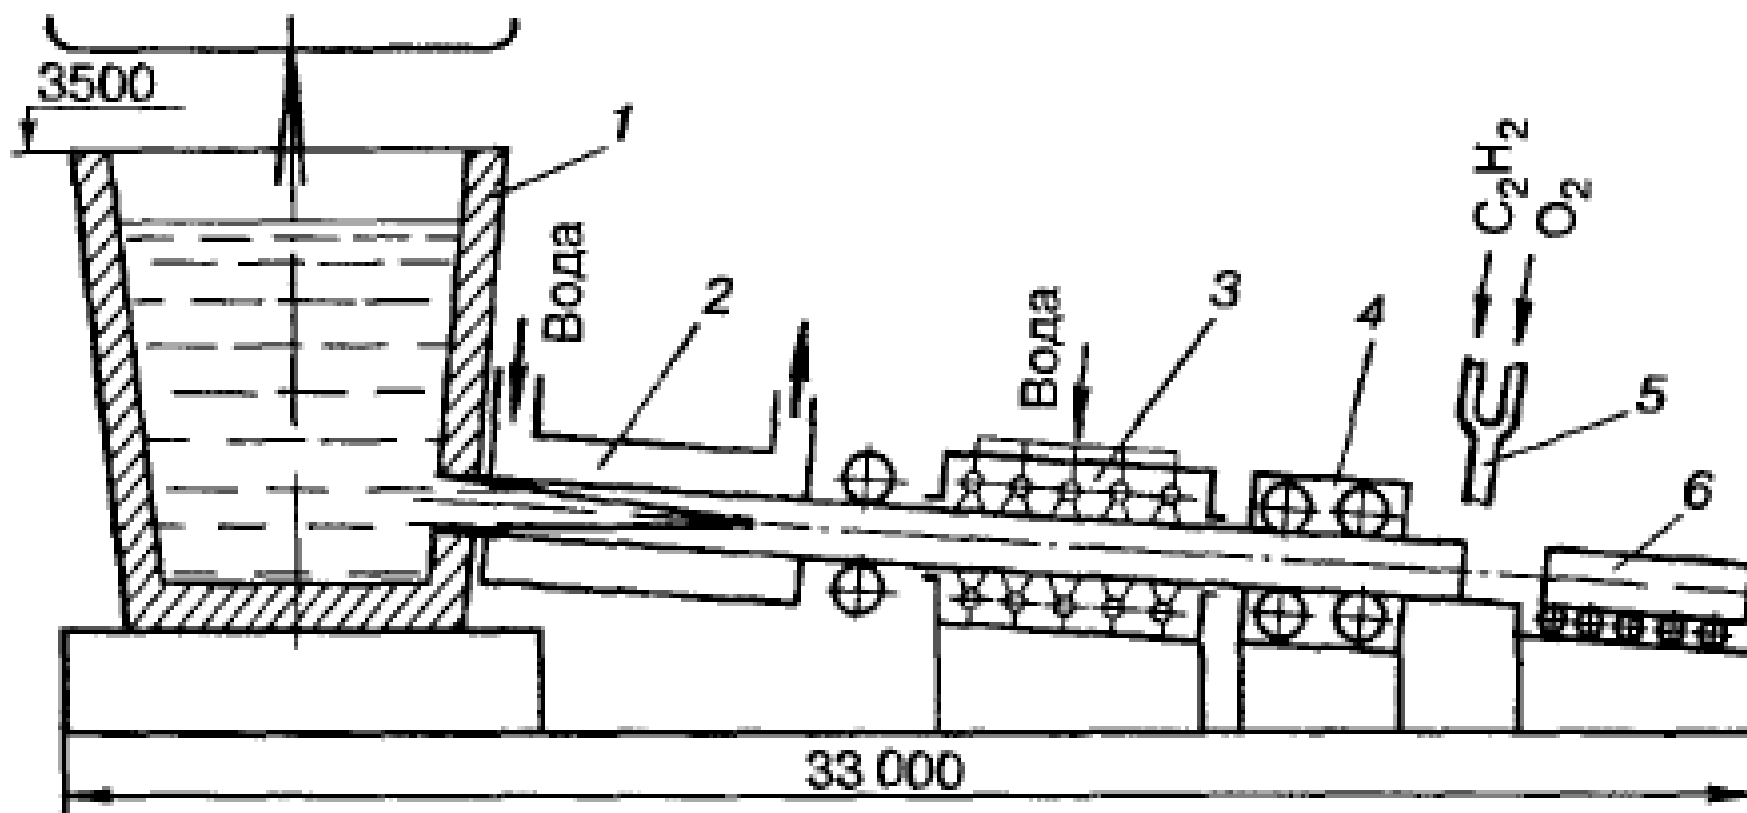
Схема машины непрерывного лиття заготовок горизонтального типа
